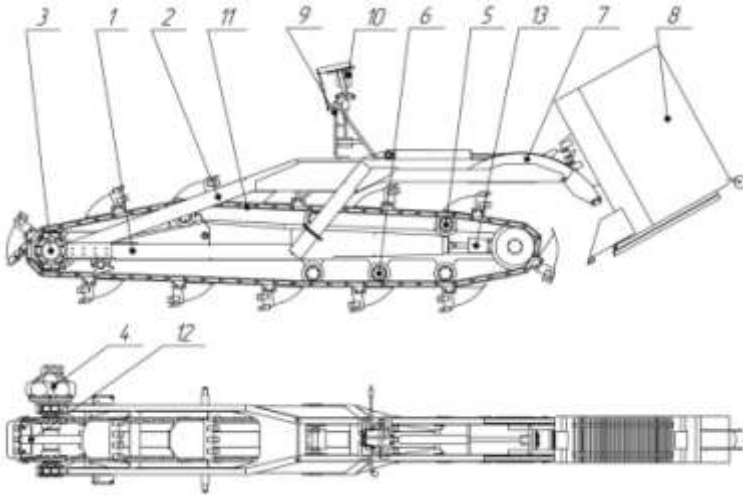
Рабочий орган: 1 – рама нижняя; 2 – рама верхняя; 3 – приводной механизм; 4 – гидромотор; 5 – поддерживающий ролик; 6 – опорный ролик; 7 – направляющий механизм; 8 – трубоукладчик; 9 – компенсирующее устройство; 10 – направляющий кронштейн; 11 – ковшовая цепь; 12 – очиститель ковшей, 13 – натяжное устройство
